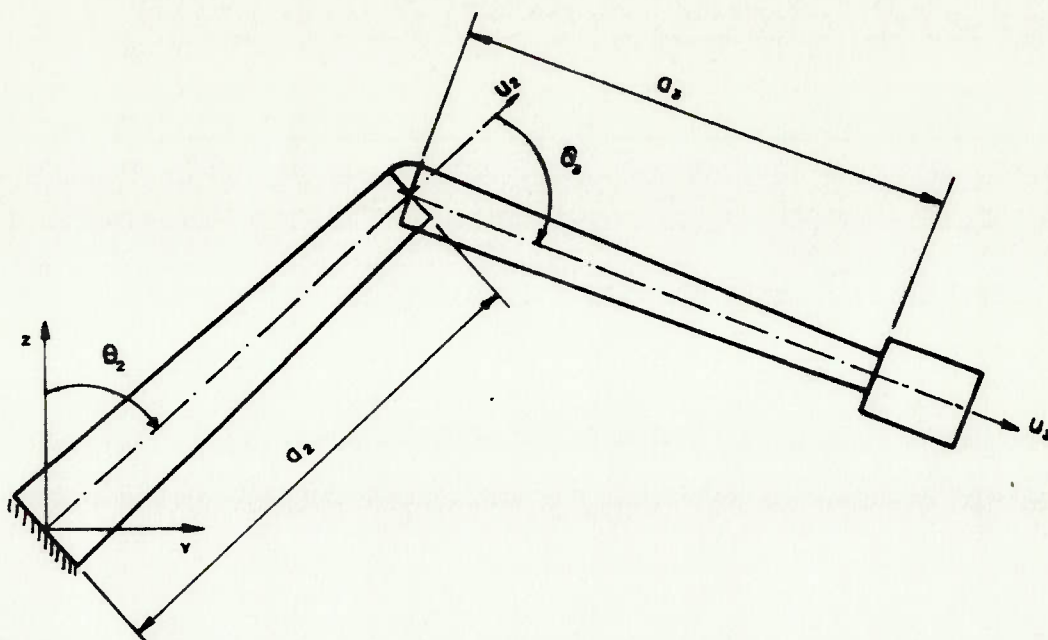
Modelo estrutural dos braços: pórtico engastado em uma configuração genérica (θ_2, θ_3)
